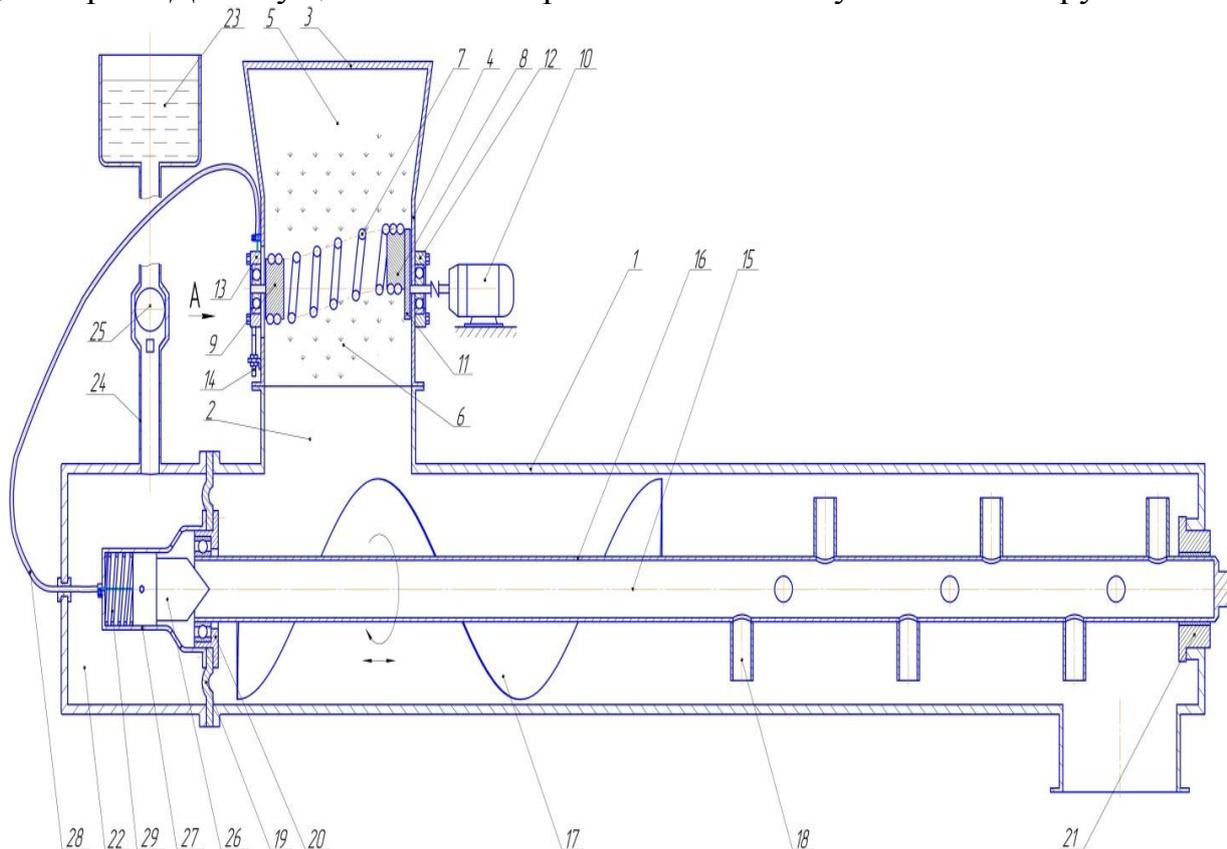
Агрегат для приготовления кормов из побочных продуктов крахмалопаточного производства
